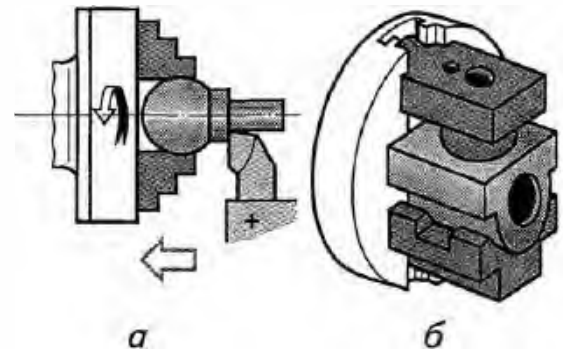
Базування заготовки з фасонною зовнішньою поверхнею:
